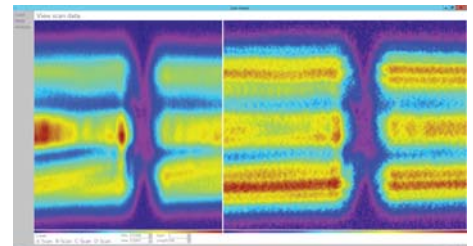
Messung an einem stumpfgeschweißten Rohrsegment
